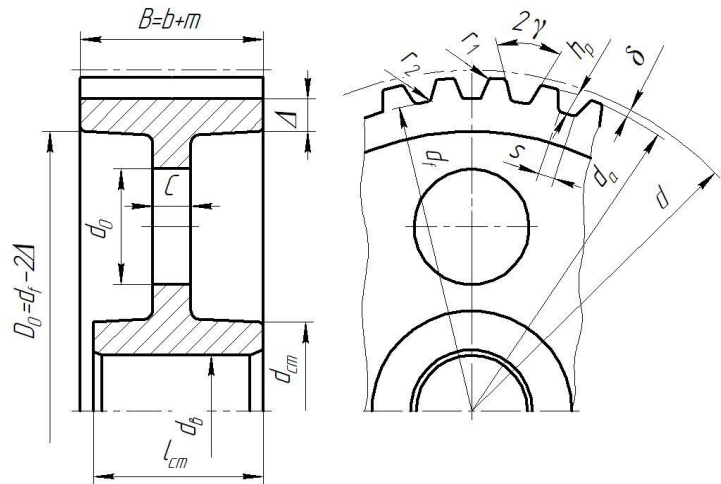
Чертеж общего вида шкива с трапецеидальными зубьями и основными размерами
